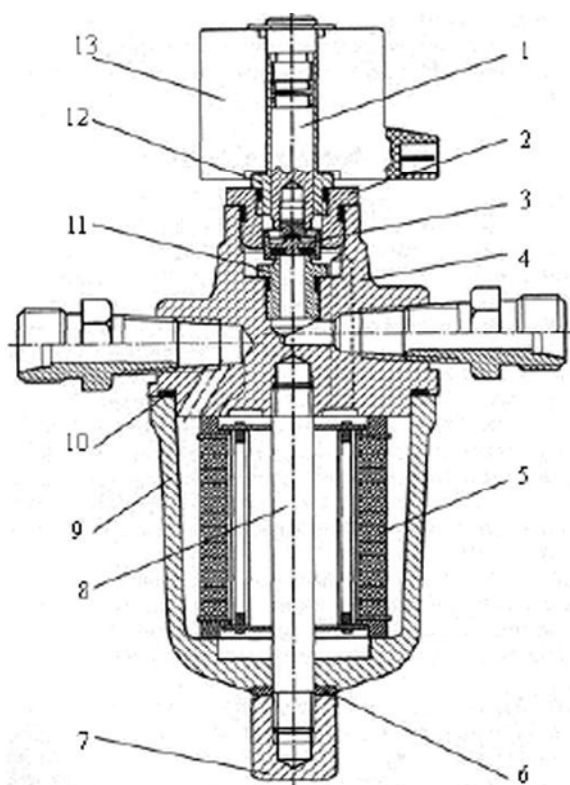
Электромагнитный клапан с фильтром газа: 1 - цилиндр; 2 - переходник; 3 - клапан дифференциальный; 4 - корпус; 5 - фильтрующий элемент; 6 - шайба; 7 - гайка колпака; 8 - шпилька; 9 - колпак фильтра; 10- кольцо уплотнительное; 11 - седло клапана; 12 - гильза; 13- катушка
